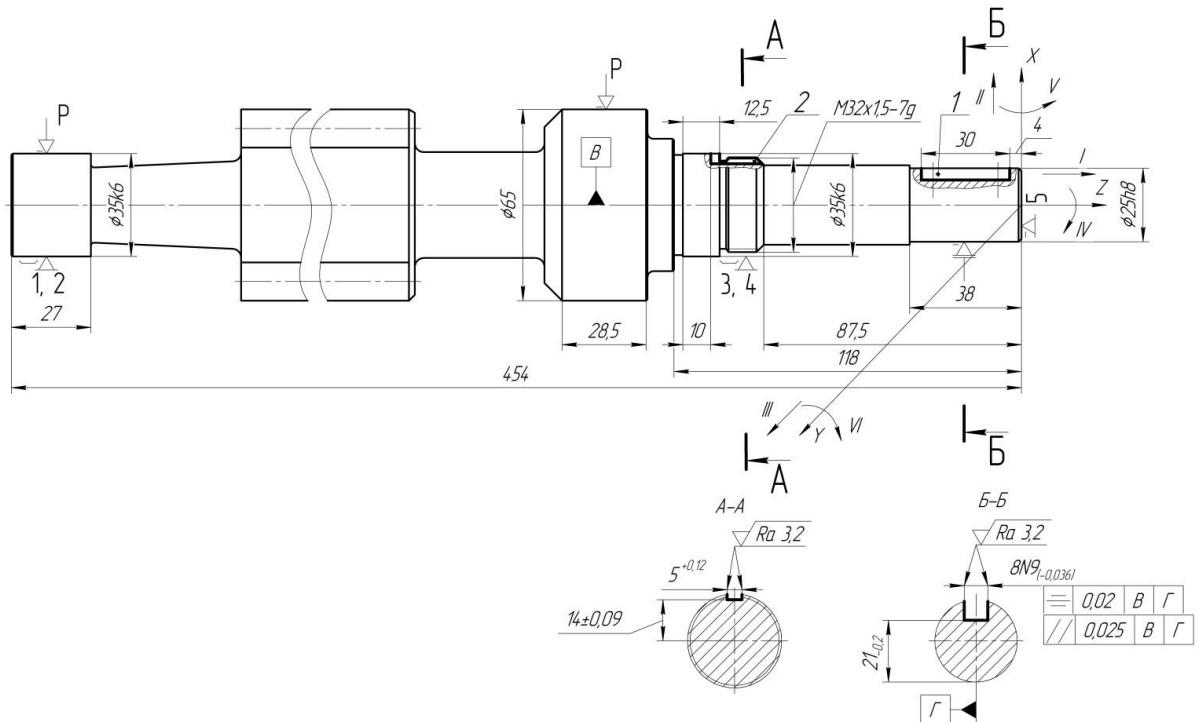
Операционный эскиз операции 030 – фрезерная с ЧПУ. Схема 1.
